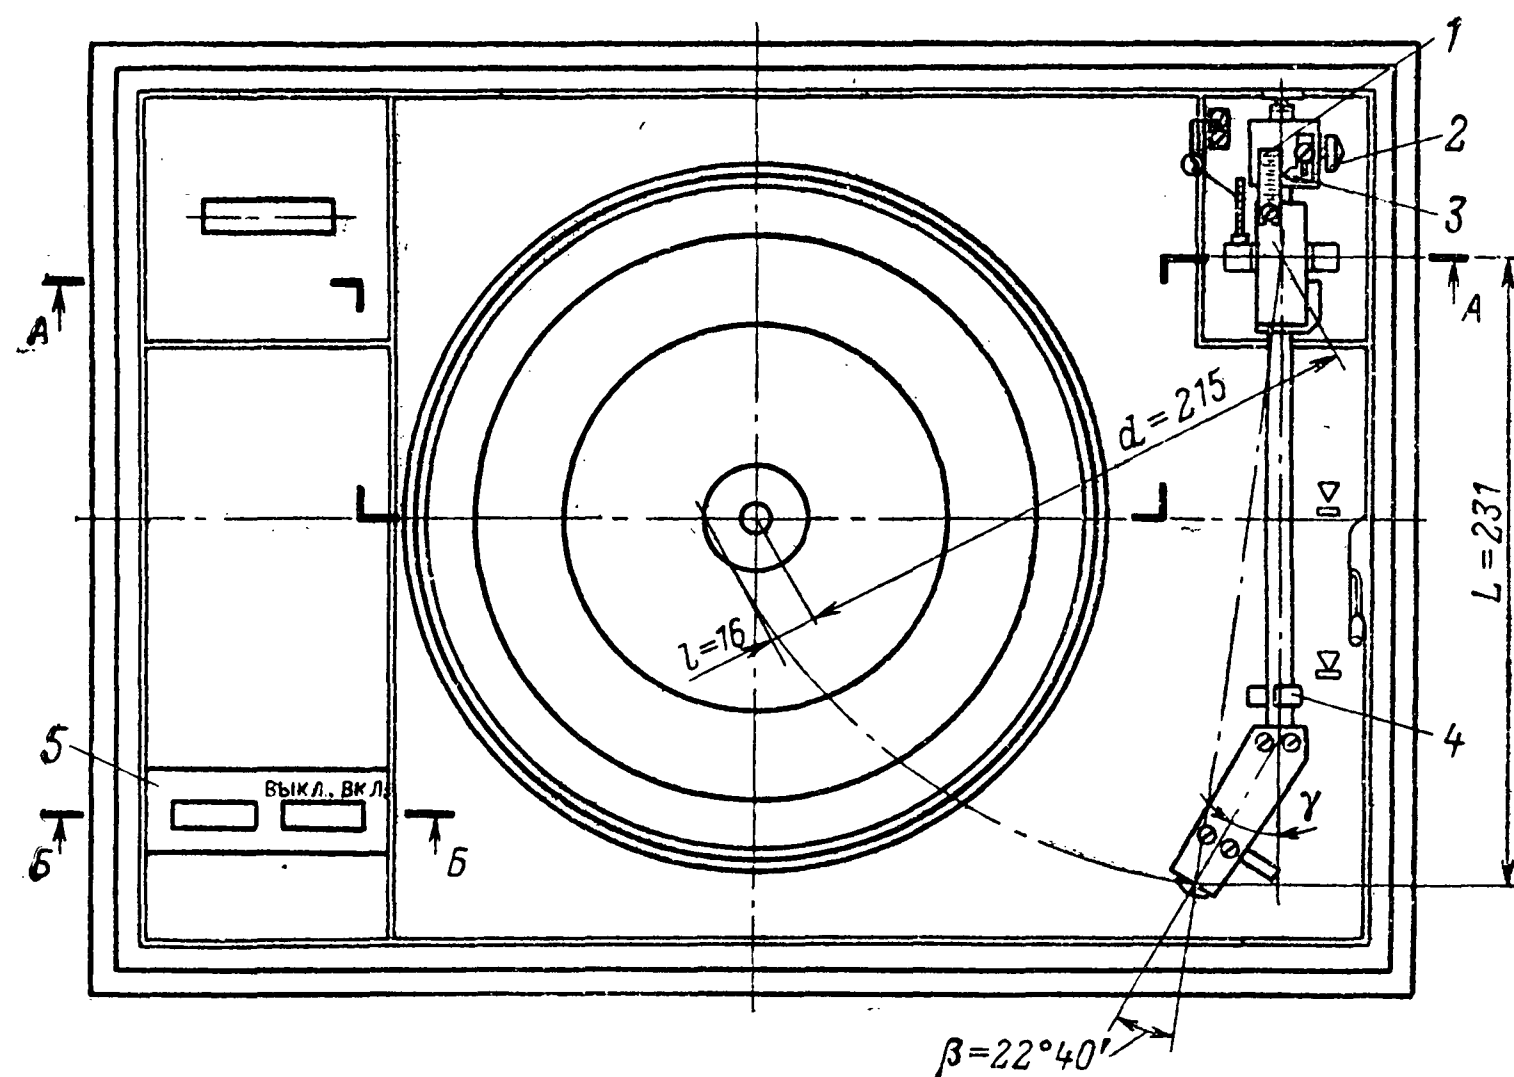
Конструкция проигрывателя. Вид сверху. Крышка не показана.
